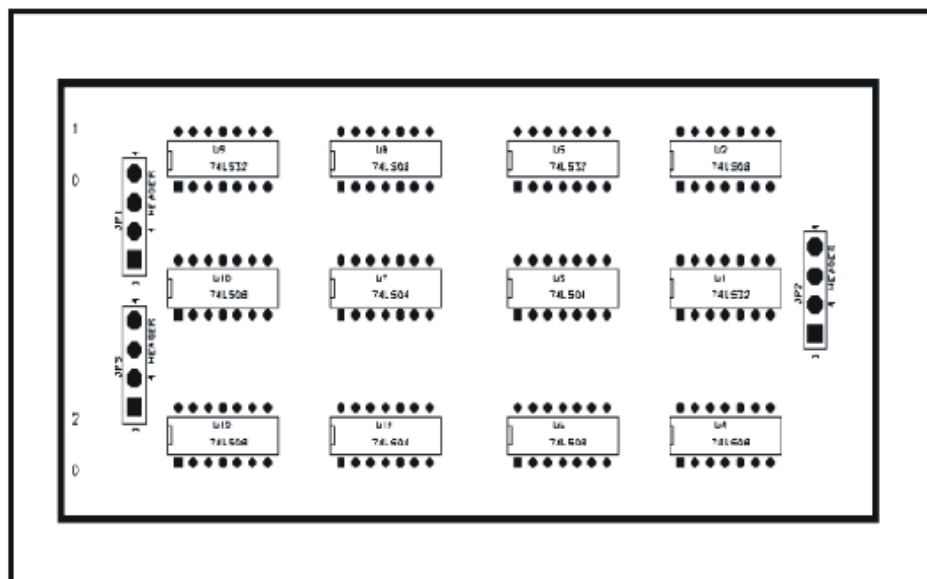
Plano de ensamblaje (cara de componentes)[40]
